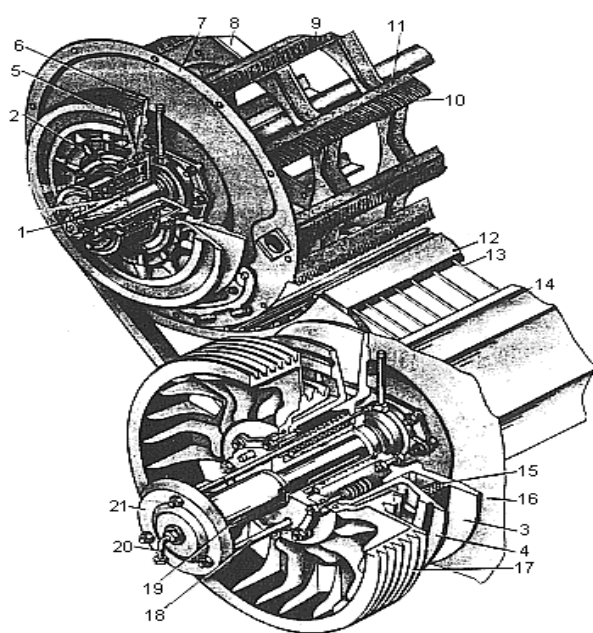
Молотильный барабан и отбойный битей зерноуборочного комбайна «Дон-1500»:
